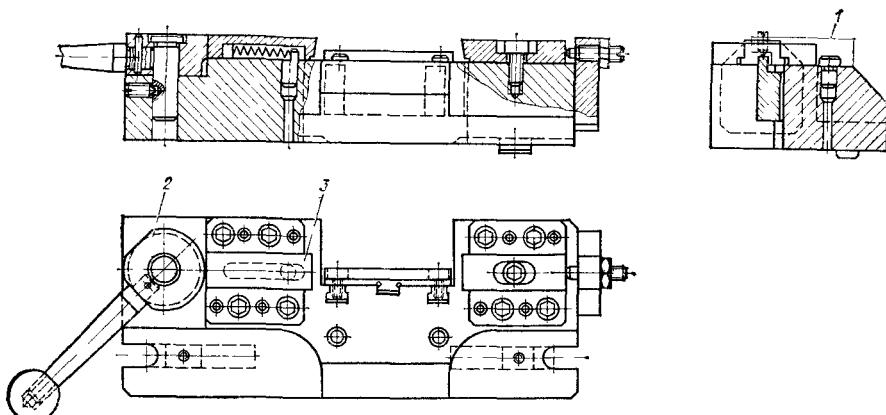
Эксцентриковое наладочное приспособление для фрезерования валиков (наладка 1 крепится эксцентриком 2 через планку 3 с боковым скосом)
